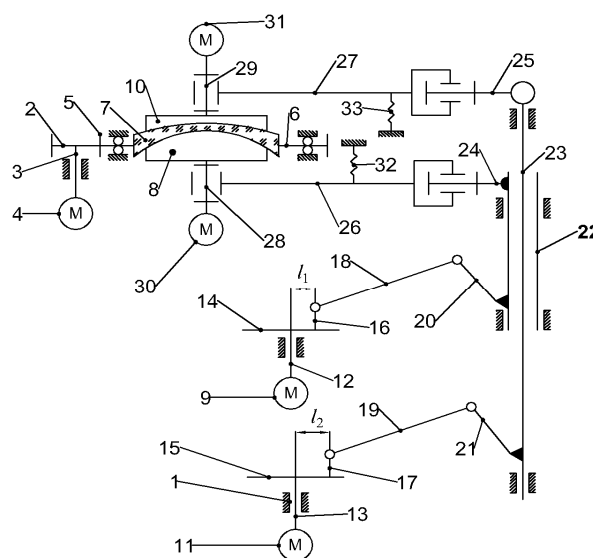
Кинематическая схема устройства для двусторонней обработки оптических деталей со сферическими поверхностями
